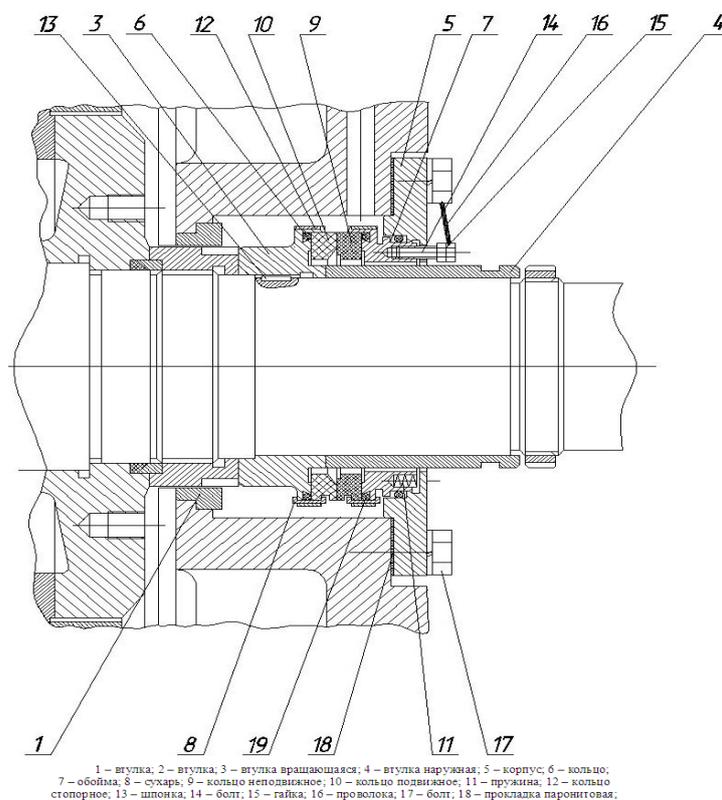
Сборочный чертёж торцевого уплотнения
